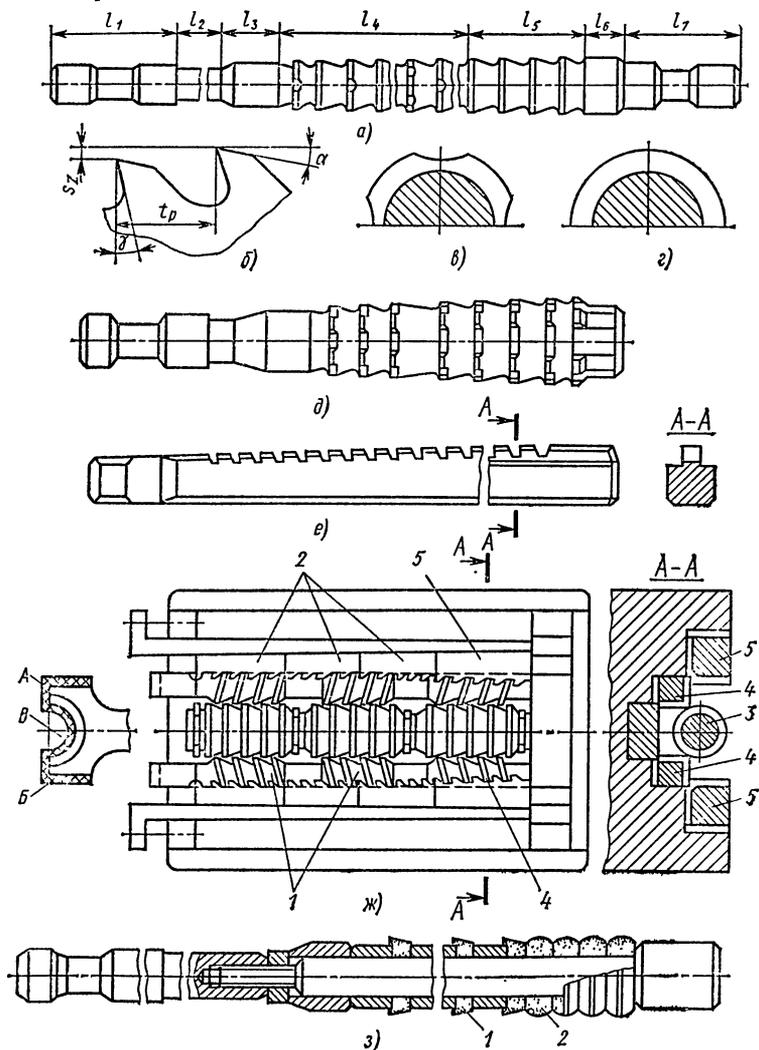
Инструменты для обработки поверхностей на протяжных станках
